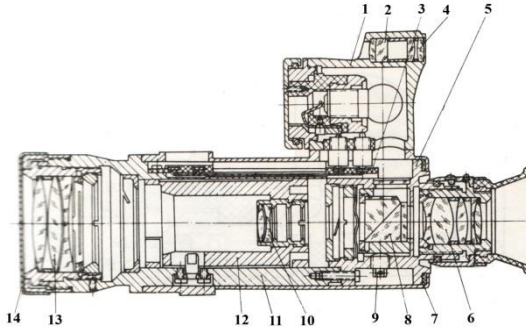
Зорова труба: 1 – освітлення; 2 – сітка з покривним склом; 3 – колодка; 4 – візир; 5 – корпус; 6 – лінзи окуляра; 7 – ковпачок; 8 – призма-сітка; 9 – гвинт; 10 – лінзи в оправі; 11 – корпус; 12 – повзун; 13 – об’єктив; 14 – ковпачок
